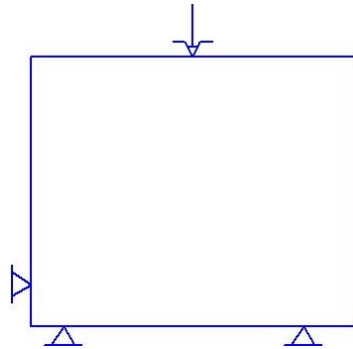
Схема базування корпусу при розточуванні отвору
